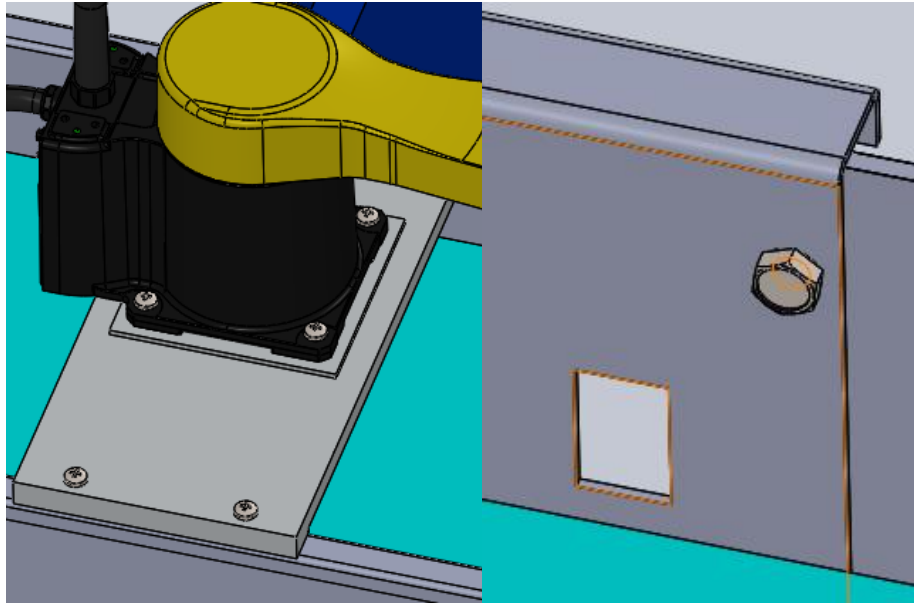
Acoblament del robot i la barrera de llum en cintes amb parets elevades. Font pròpia
